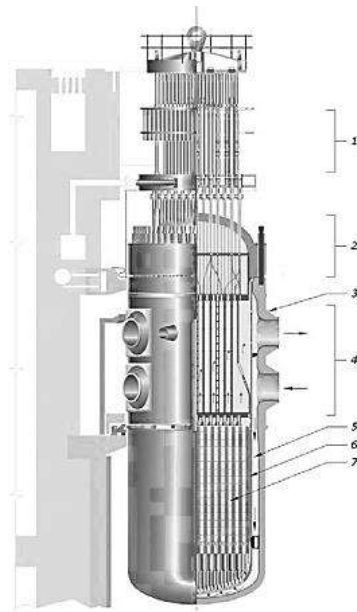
Конструкция реактора ВВЭР-1000: 1 – приводы системы управления и защиты; 2 – крышка реактора; 3 – корпус реактора; 4 – блок защитных труб; 5 – шахта; 6 – перегородка активной зоны; 7 – тепловыделяющие сборки, стержни управления
